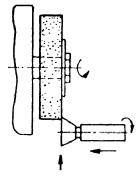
Схема обработки наружной поверхности кругов прямого профиля на токарном станке
